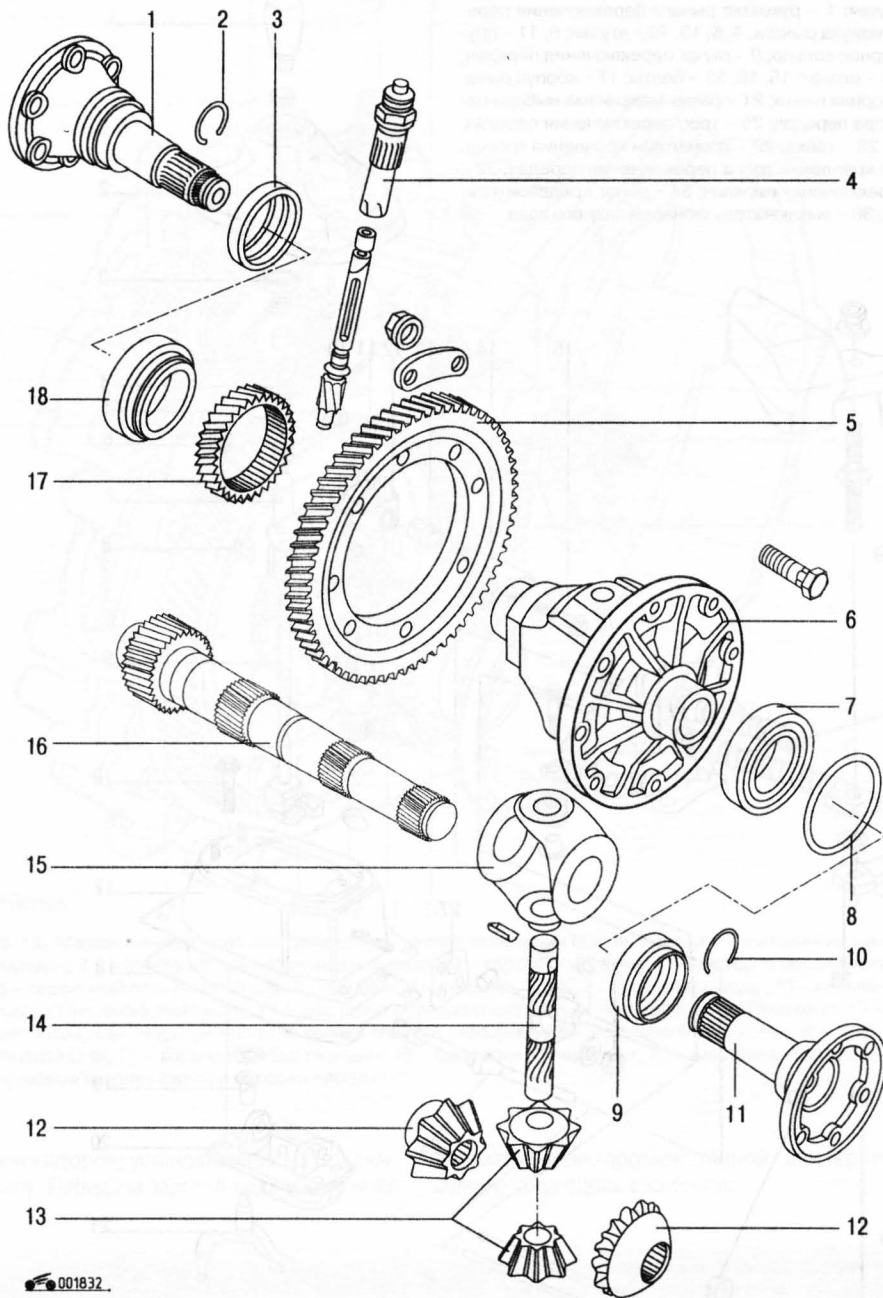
Главная передача и дифференциал: 1, 11 – фланцы полуоси; 2 – стопорное кольцо; 3, 9 – сальники; 4 – привод спидометра; 5 – ведомая шестерня главной передачи; 6 – корпус дифференциала; 7, 18 – подшипники дифференциала; 8 – упорная шайба; 10 – стопорное кольцо; 12 – полуосевая шестерня; 13 – сателлиты; 14 – ось сателлитов; 15 – сепаратор; 16 – вторичный вал; 17 – шестерня привода спидометра
